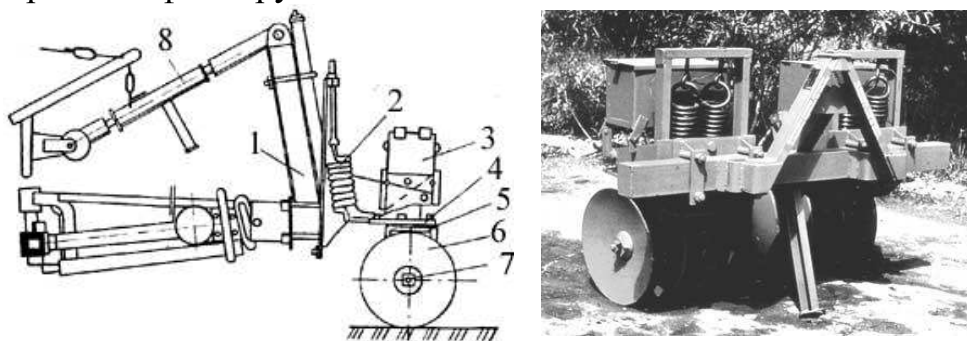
Культиватор лесной бороздной КЛБ-1,7: 1 – рама; 2 – амортизационное устройство; 3 – балластный ящик; 4 – неподвижная плита; 5 – нижняя горизонтальная плита; 6 – батареи дисков; 7 – ось батарей
